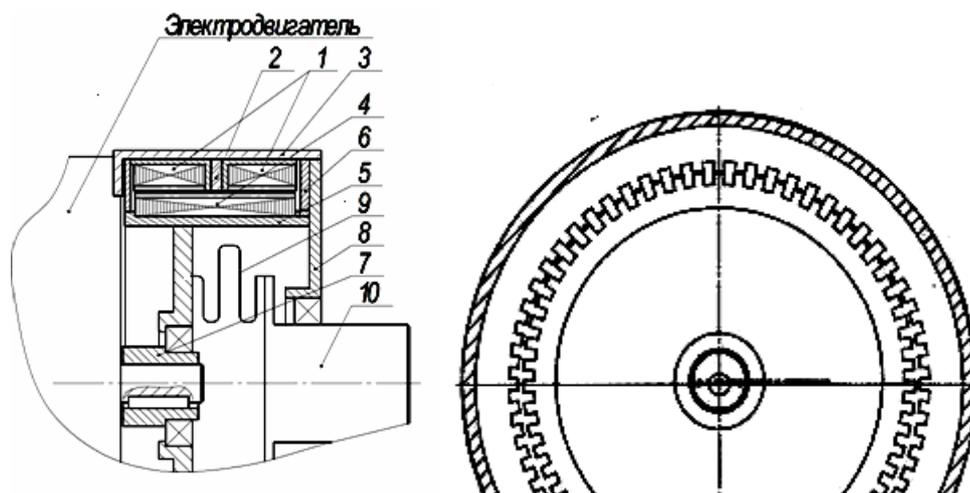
Устройство механической передачи с использованием магнитных сил притяжения
